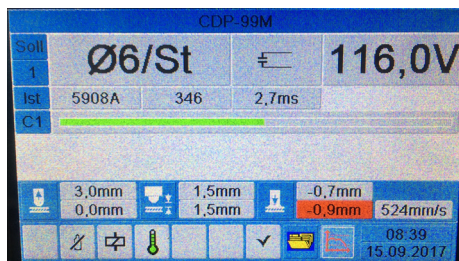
oben: Wegemessung ohne Prozessüberwach (ohne Aufzeichnung)
